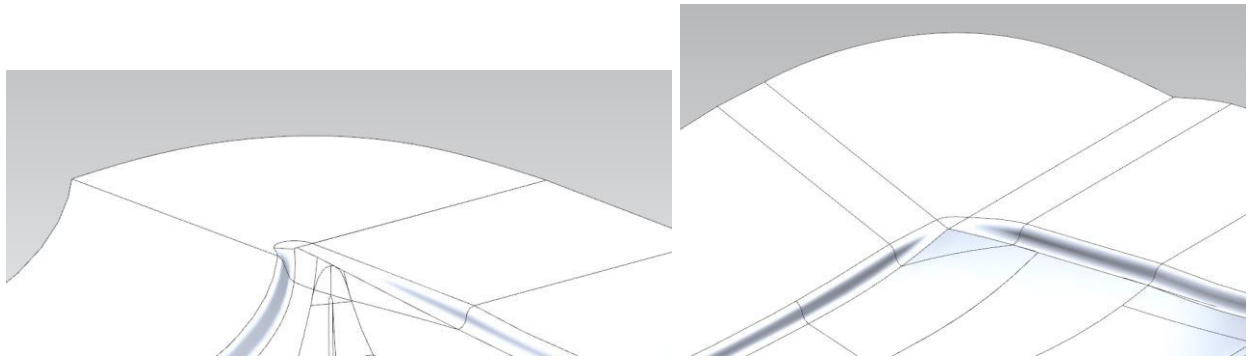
Foto 76. Esquinas de la matriz tras realizar el rebaje.
